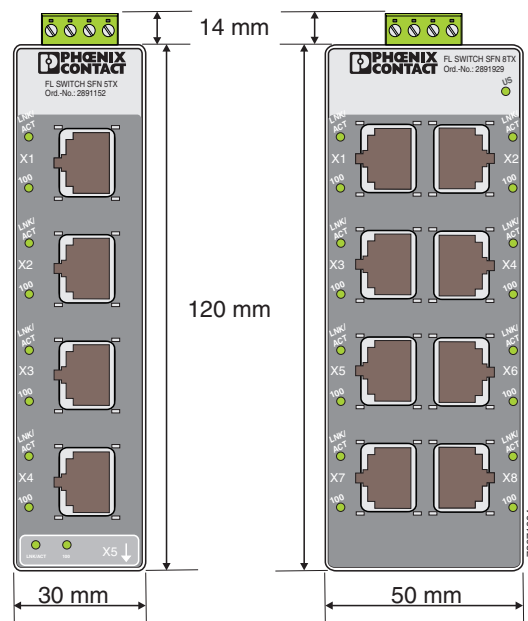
Dimensiones de la carcasa de FL SWITCH SFN ...
